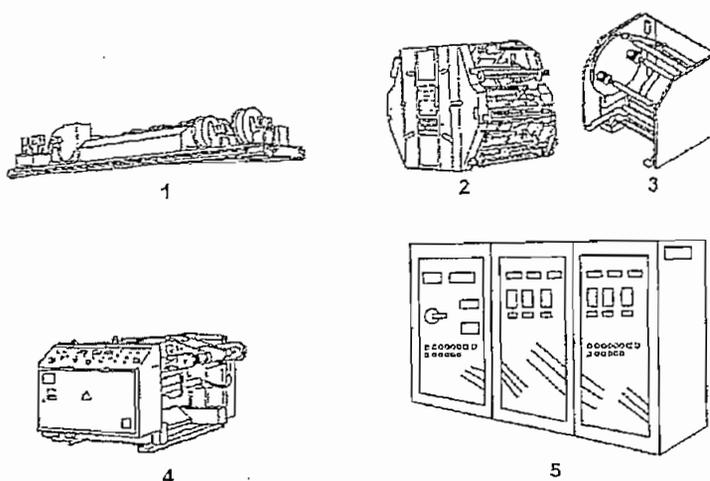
Sistemas de máquina impresora 1 puente y túnel de secado, 2 unidad de impresión, 3 rebobinador, 4 desbobinador, 5 gabinete eléctrico (ref.12)
